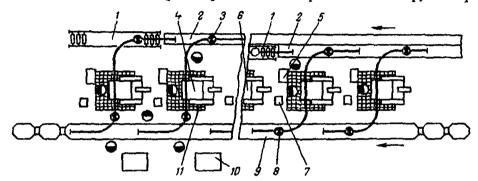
Схема планировки рабочего места формовщика средних отливок при групповом расположении формовочных машин:
